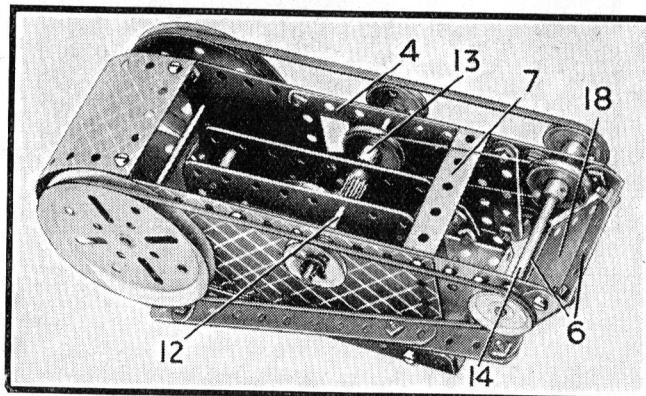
Le tank de la fig. 4, vu par en dessous.
